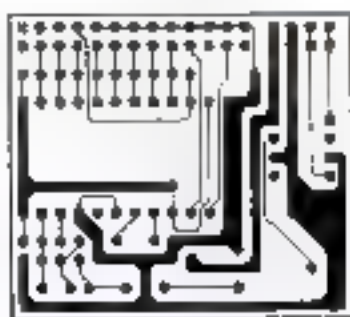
Circuit imprimé vu côté soudures.
